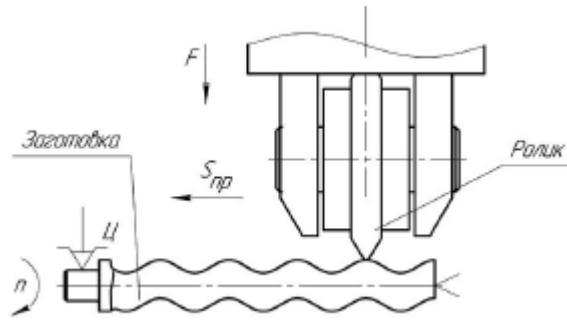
Схема обкатування ротора гвинтового дозатора
